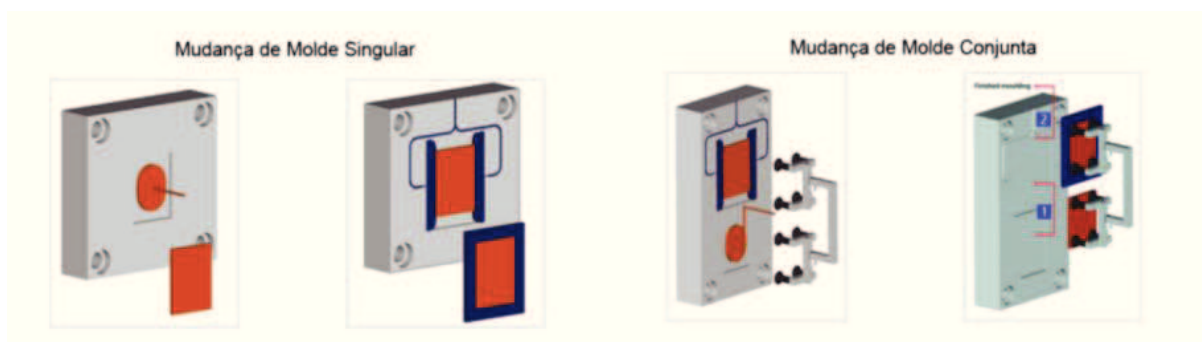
Técnicas de mudança de molde singular ou conjunta [17].
